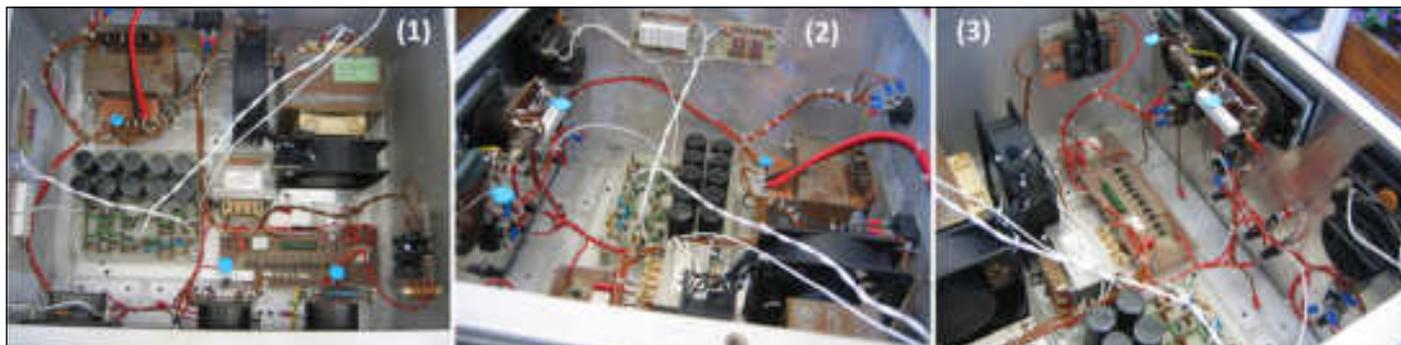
Vues générales de la disposition des éléments et du câblage intérieur
